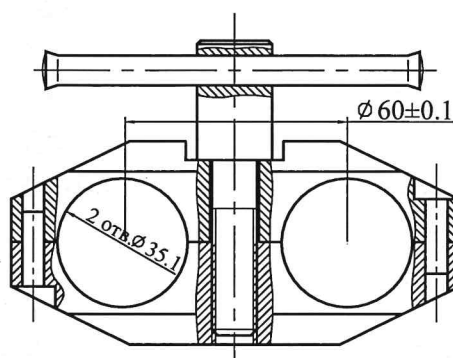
Приспособление для установки клапана черт. ОК-0112СБ.
